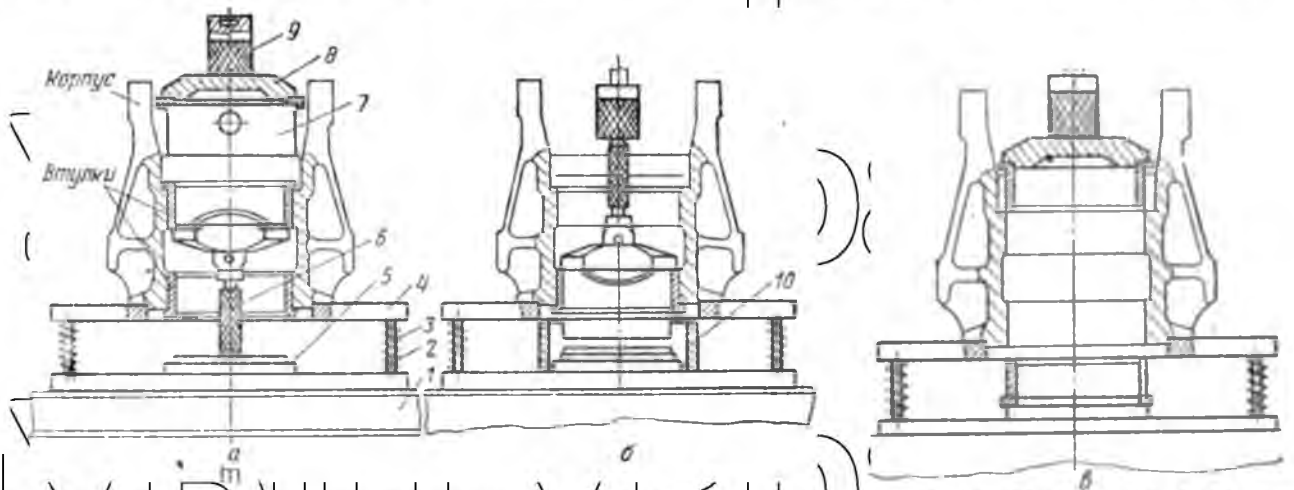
Положення пристосування ОР-6305 при випресуванні і запресуванні втулок горизонтального шарніра: а — випресування верхньої втулки; б — випресування нижньої втулки; в — запресування втулок. 1 — основа; 2 — пружина; 3 — штанга; 4 — плита; 5 — фіксатор; 6 — оправка; 7, 8 и 9 — наставки; 10 — підставка.
